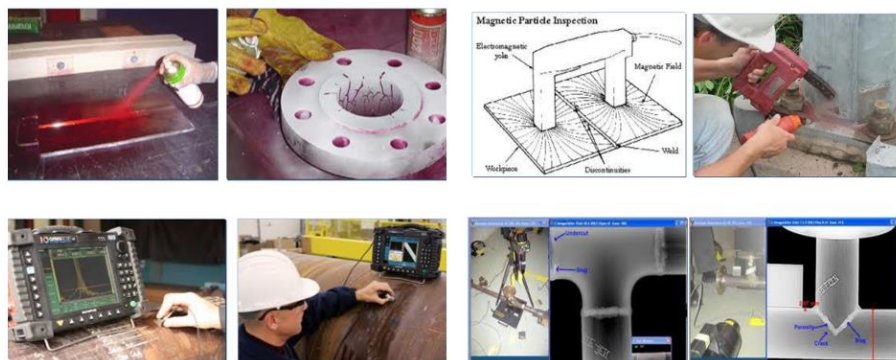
END em soldadura – Formação CMM: Marcação CE [37]
